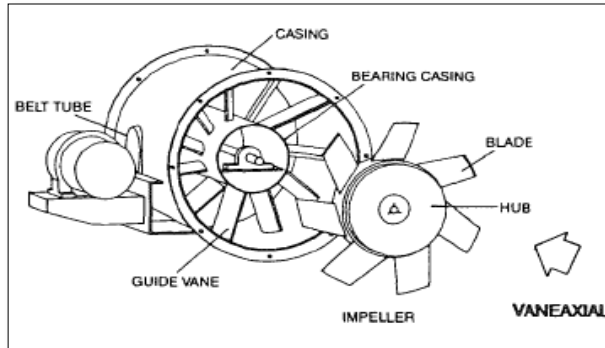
PARTES DE UN MOTOR AXIAL TUBULAR
